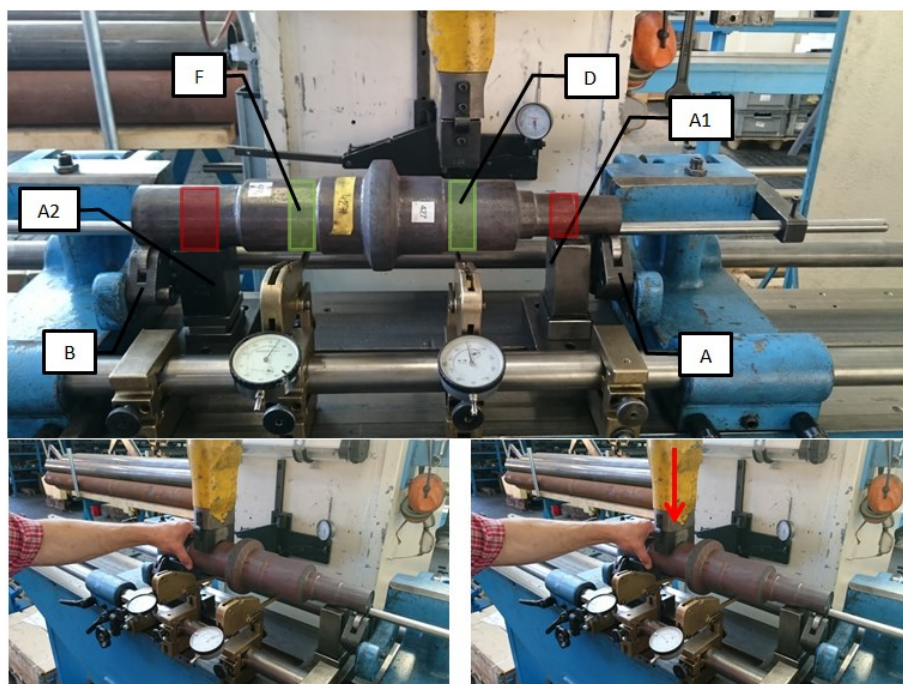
Richtvorrichtung mit eingelegter Getriebewelle (oben); Positionieren der Welle vor dem Richten, damit der Druckstempel im Bereich F aufliegt (links unten), Richtbiegen der Welle durch Drücken mit dem Stempel auf die Fläche F (rechts unten)
